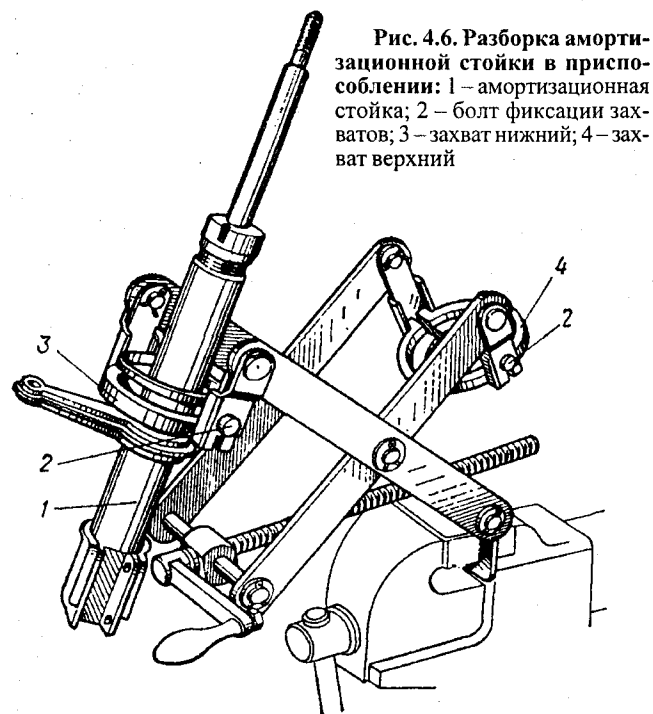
Разборка амортизационной стойки в приспособлении: 1 – амортизационная стойка; 2 – болт фиксации захватов; 3 – захват нижний; 4 – захват верхний
